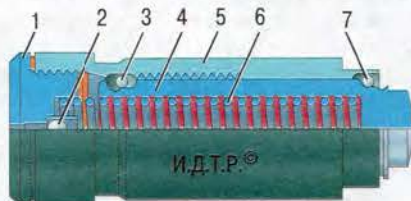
Гидронатяжитель цепи: 1 – резьбовая пробка; 2 – обратный шариковый клапан; 3 – запорный клапан; 4 – плунжер; 5 – корпус; 6 – пружина; 7 – стопорное кольцо
